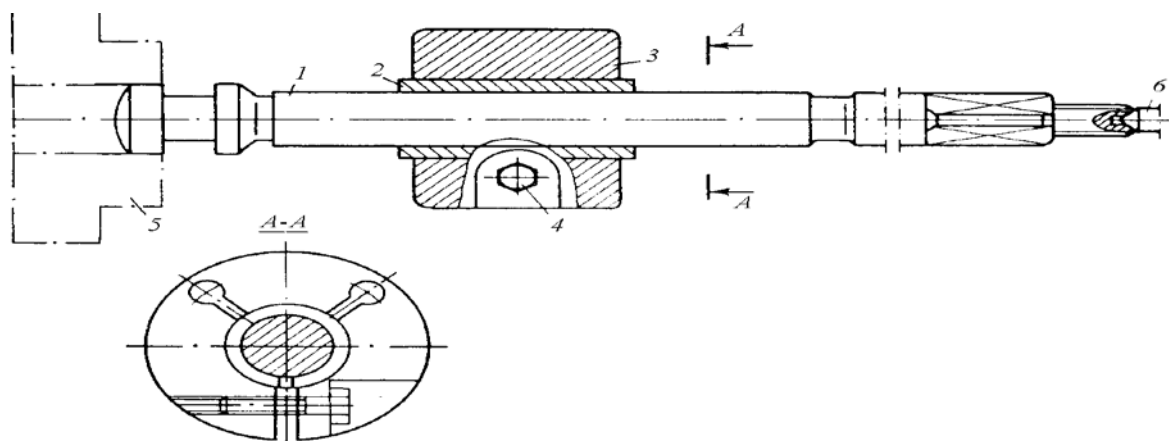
Приспособление для притирки уплотнительных поверхностей шпинделя:
